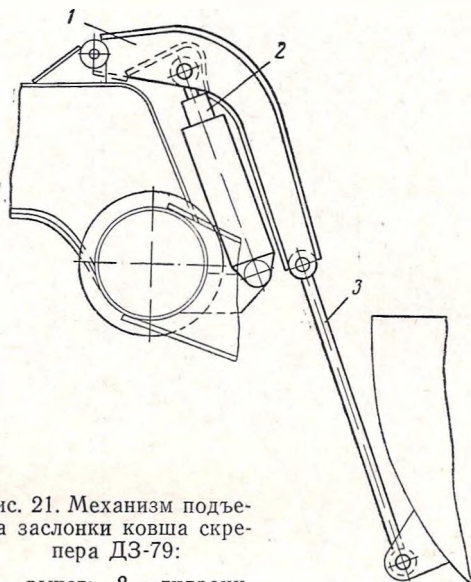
Механизм подъема заслонки ковша скрепера ДЗ-79:
